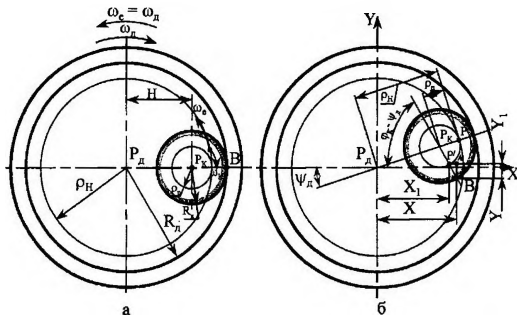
Схема для визначення траєкторії руху абразивних зерен відносно деталі при внутрішньому шліфуванні для випадку обертання деталі і круга в одному напрямку
